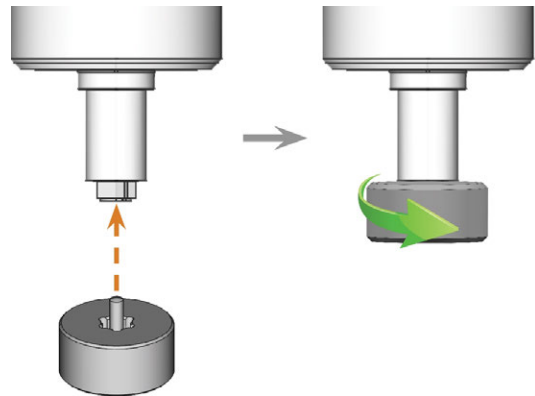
Die Spannzange mit der Rändelmutter festziehen; Aussparung in Rändelmutter orange markiert
